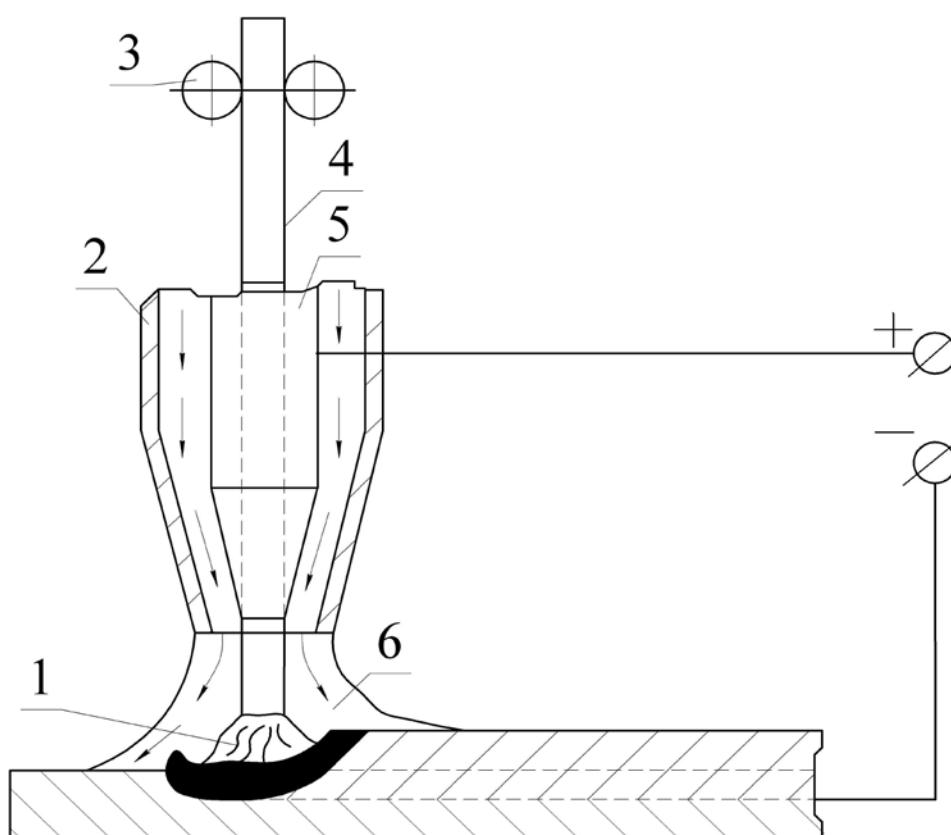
Схема дуговой сварки в углекислом газе плавящимся электродом
